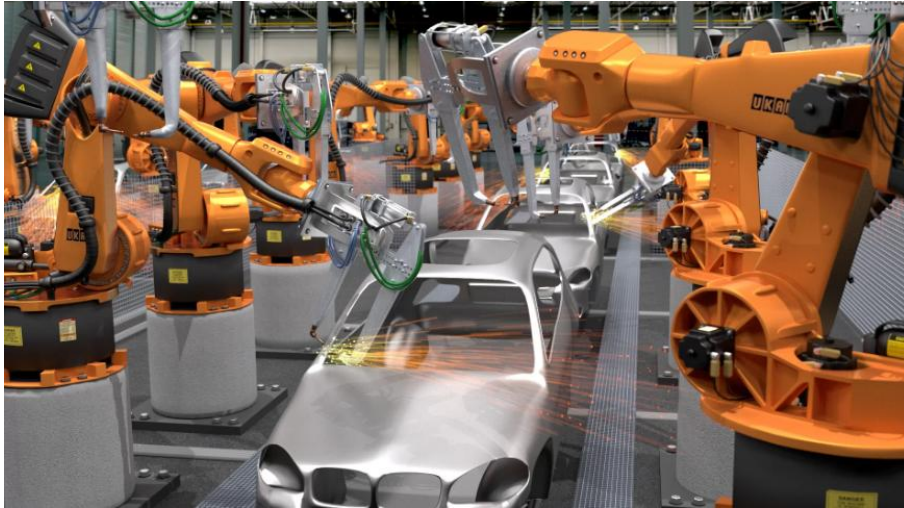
Robôs industriais de soldadura automática na indústria automóvel.
